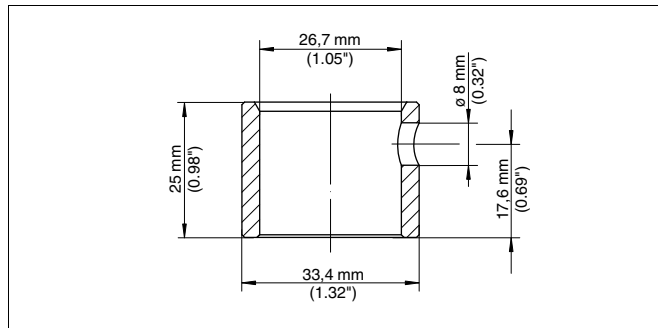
Maße Einschweißstutzen PMC 1"
